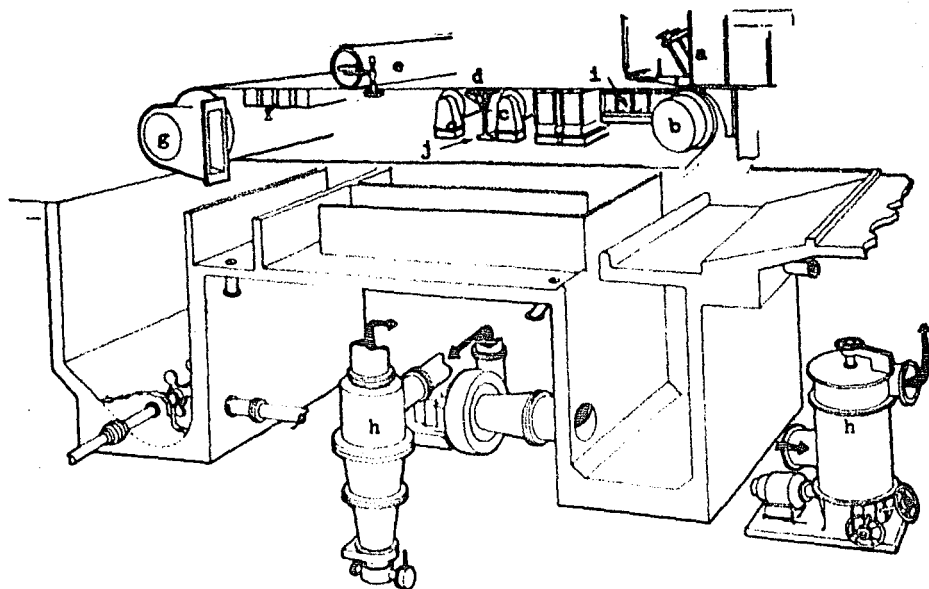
Fourdrinier moderno. a, caja de alimentación; b, rodillo de pecho; c, rodillos de la mesa de fabricación; d, tela de alambre; e, dandy-roll; f, cajas de succión; g, rodillo de succión; h, depuradores; i, formadores; j, samparas.
